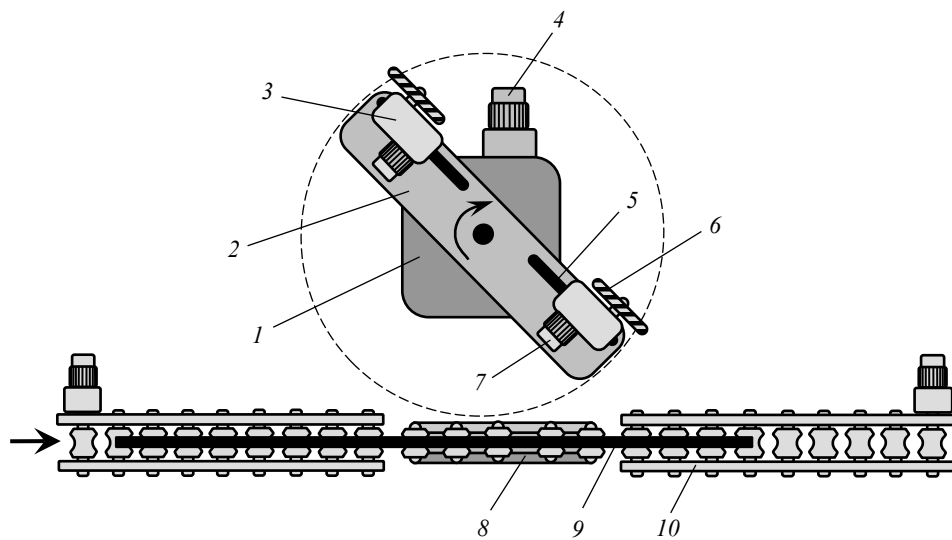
Летюча пила для порізки труб: 1 — нерухома платформа; 2 — обертаний стіл; 3 — каретка; 4 — електропривід мехпнізму повороту стола; 5 — напрямна каретка; 6 — ріжучий диск; 7 — електропривод ріжучого диска; 8 — механізм підйому труби; 9 — труба; 10 — секція рольгангу
